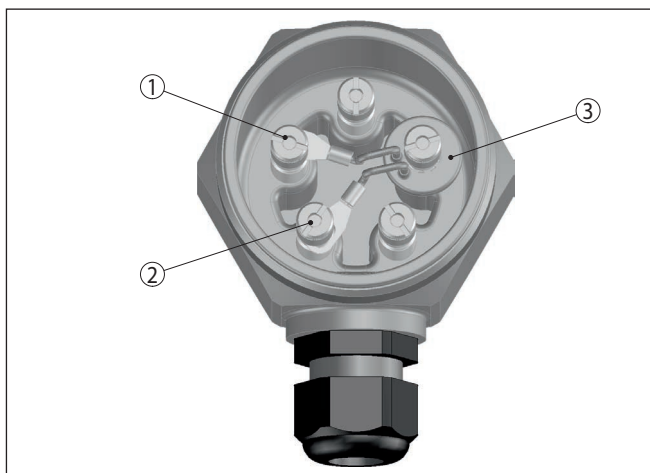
Montage van de extra elektronica voor kabelbreukbewaking
